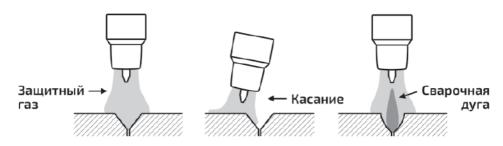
Процесс образования сварочной дуги.
